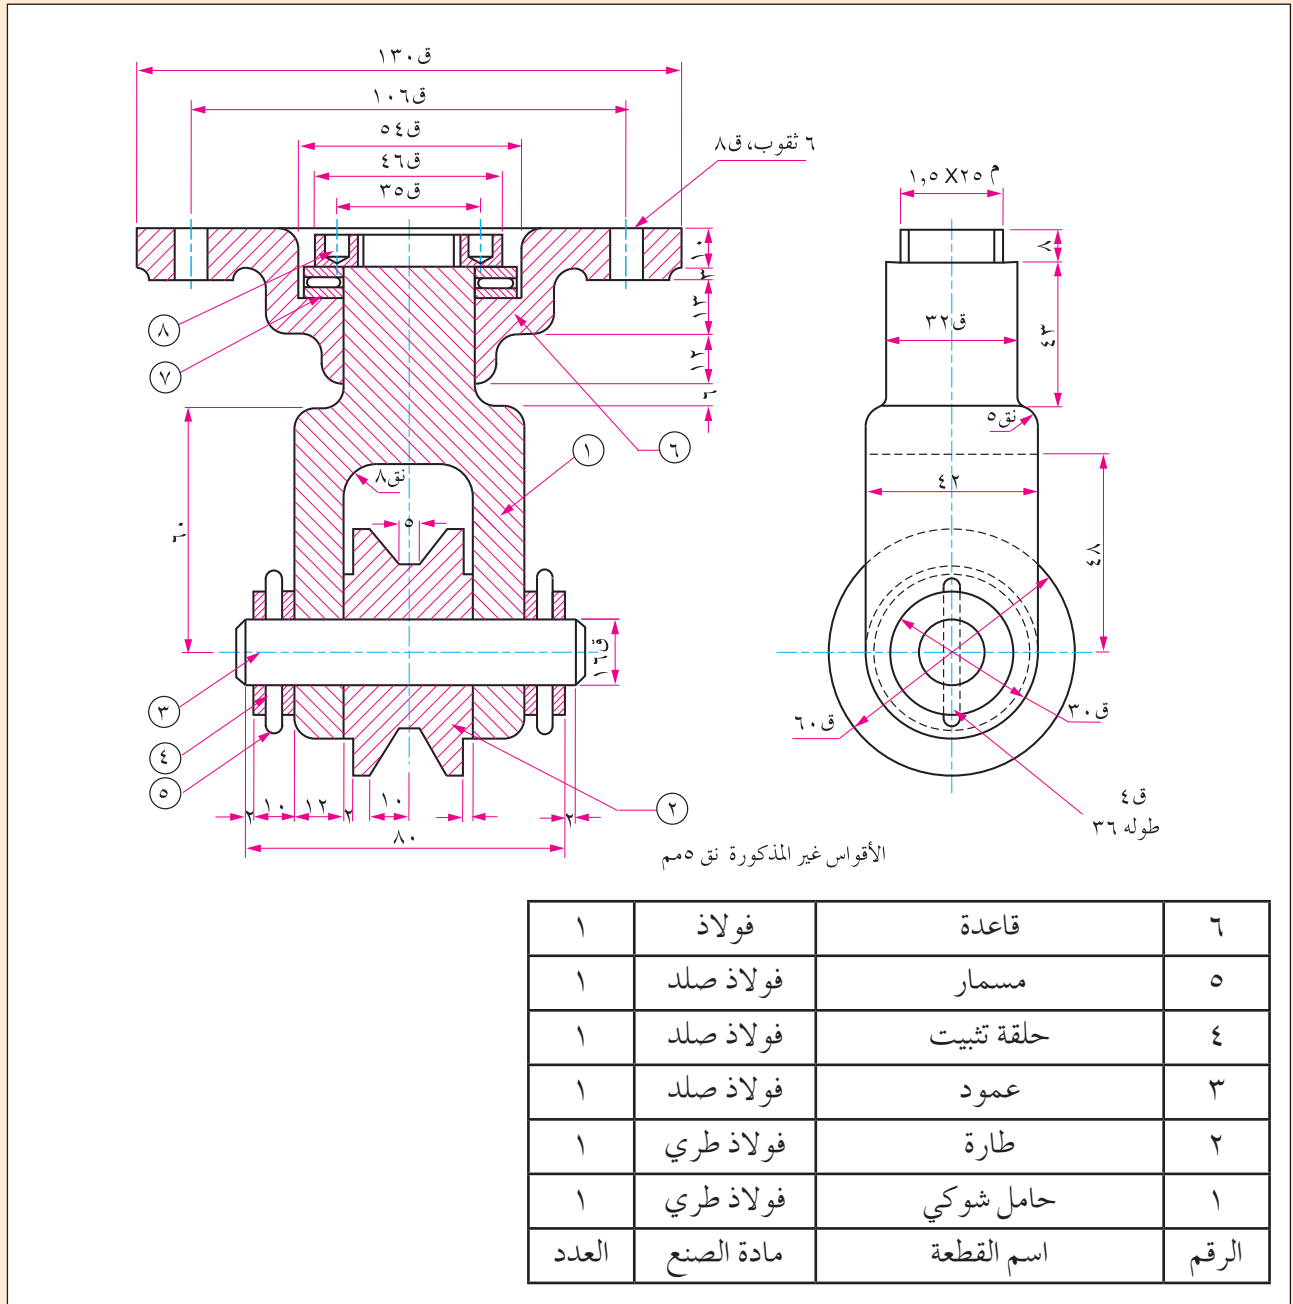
مسقط أمامي مجمّع لساحبة.
